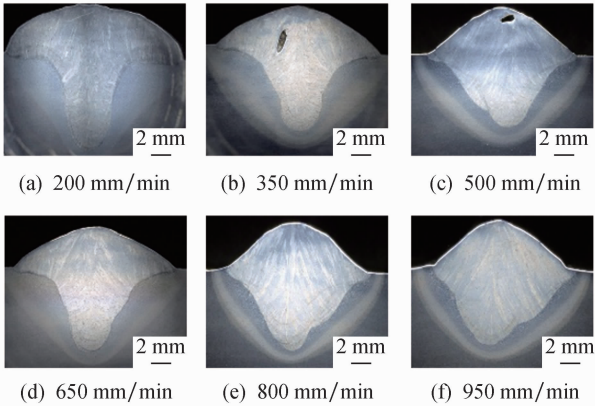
深熔 GMAW 不同焊接速度下的接头截面形貌
